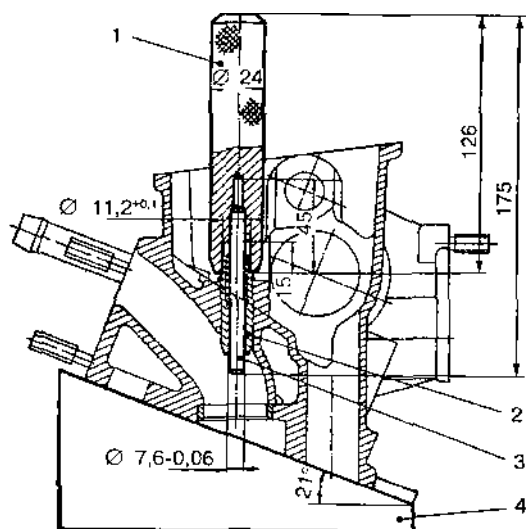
Оправка М9840-748 для запрессовки направляющих втулок клапанов:
